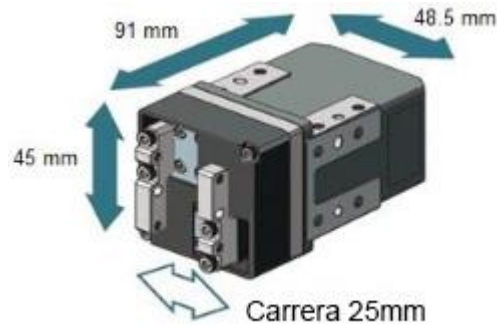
Compactas dimensiones con una carrera de 25mm (12.5 mm por lado).
